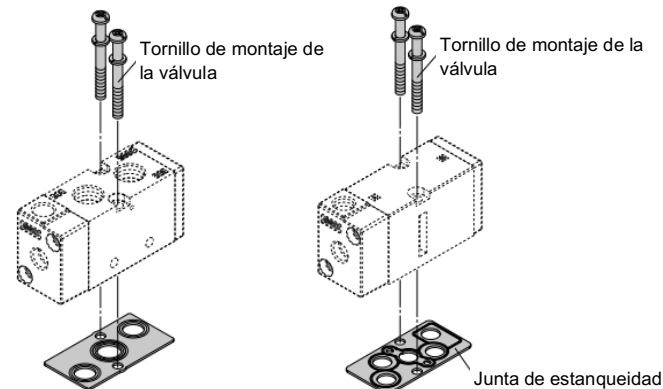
Para montaje individual (izquierda) y montaje en placa base (derecha)
